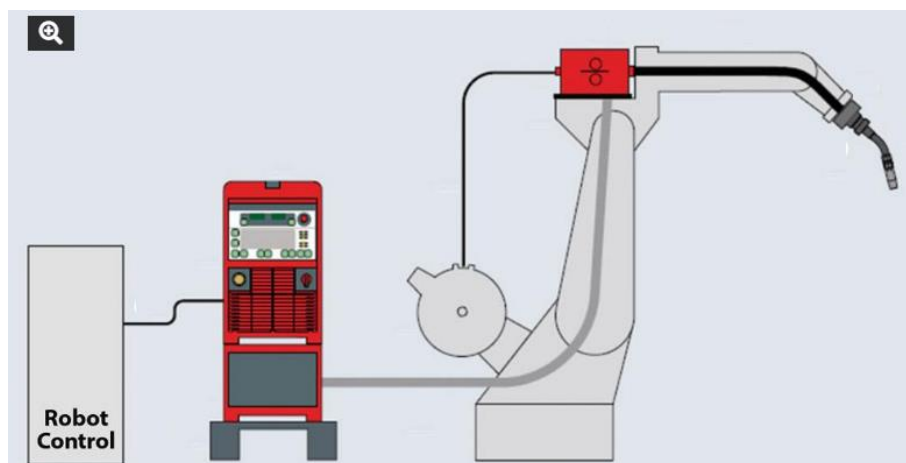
Esquema estación de soldadura robotizada
